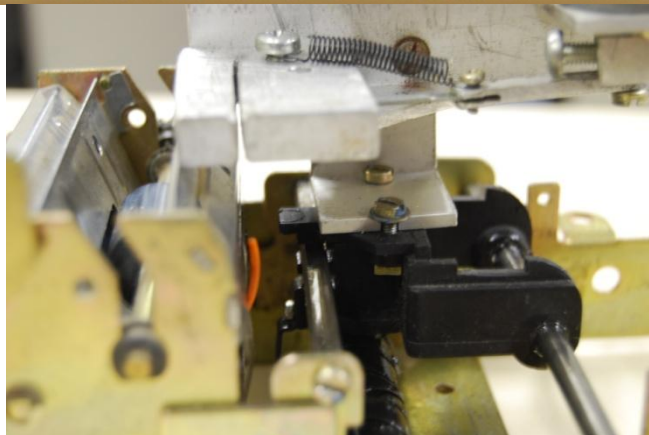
Detalhe do acoplamento entre o cabeçote de impressão e o chassis
